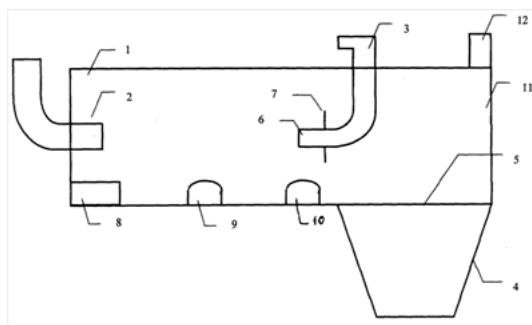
Горизонтальный коллектор-пылеуловитель: 1 – цилиндрический корпус; 2 – патрубок вывода чистого газа; 3 – патрубок ввода загрязненного газа; 4 – конический пылесборник; 5 – продольная прорезь; 6 – осевой выход загрязненного газа; 7 – отбойная шайба; 8, 9, 10 – дополнительные патрубки ввода загрязненного газа; 11 – торец цилиндрического корпуса; 12 – дополнительный патрубок вывода чистого газа
